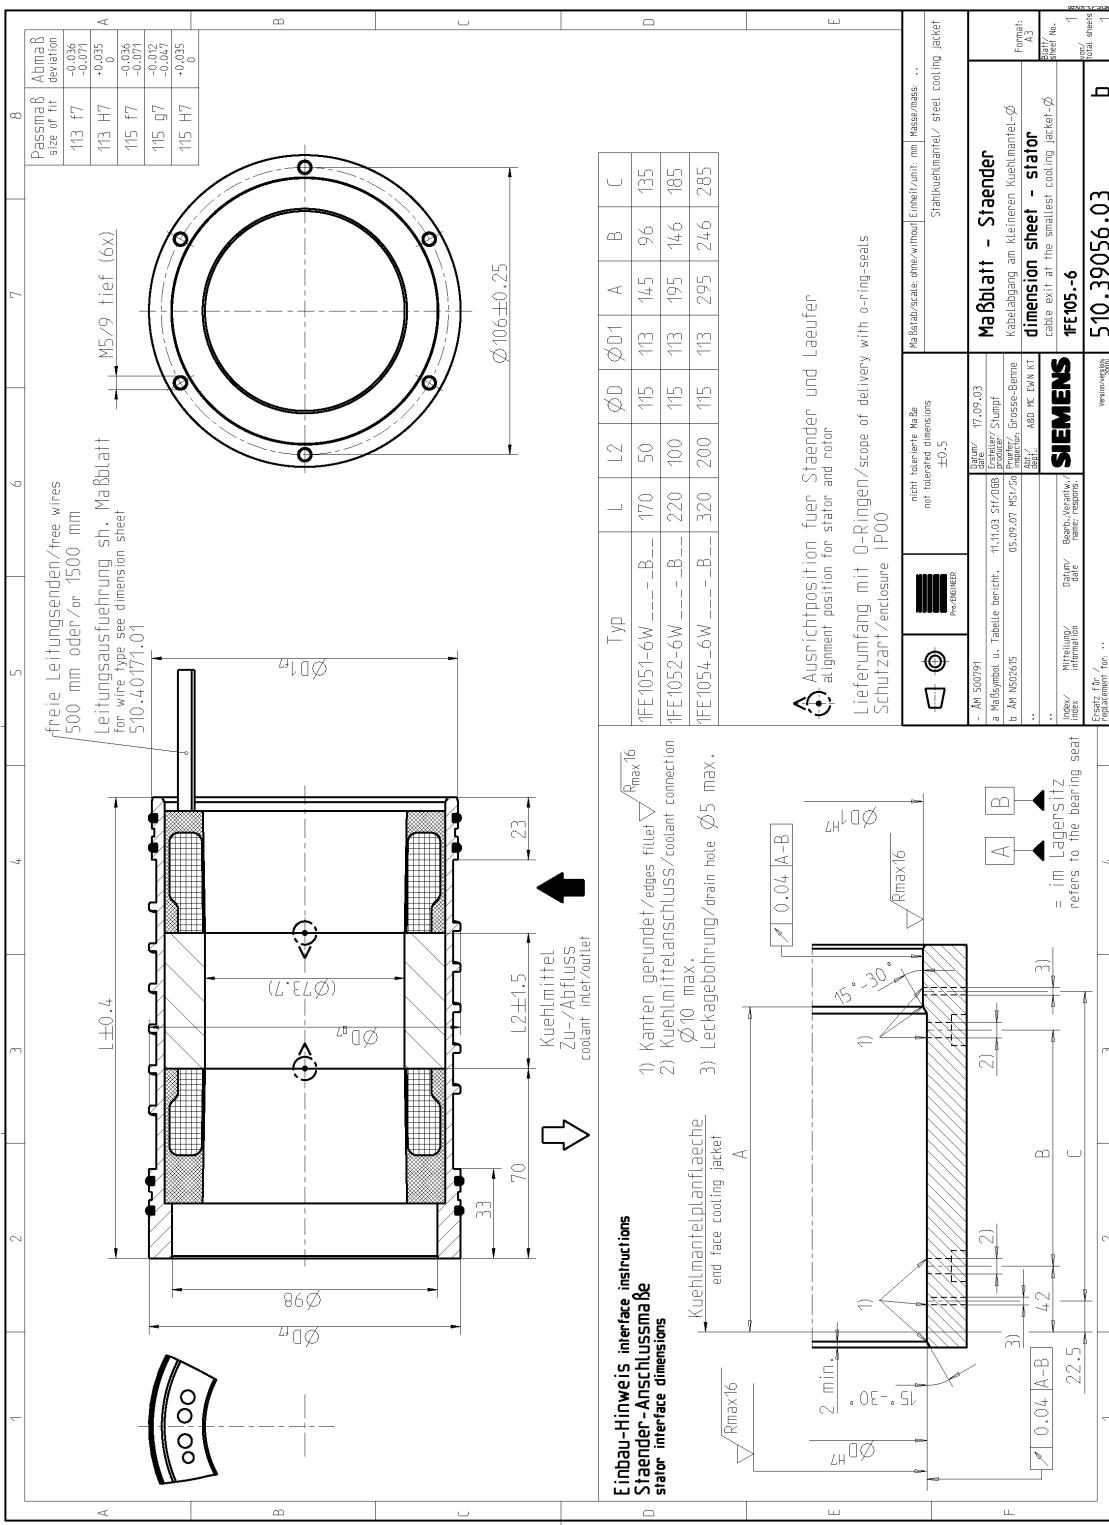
1FE105□-6, Ständer mit Kühlmantel, Kabelabgang am kleineren Kühlmanteldurchmesser
